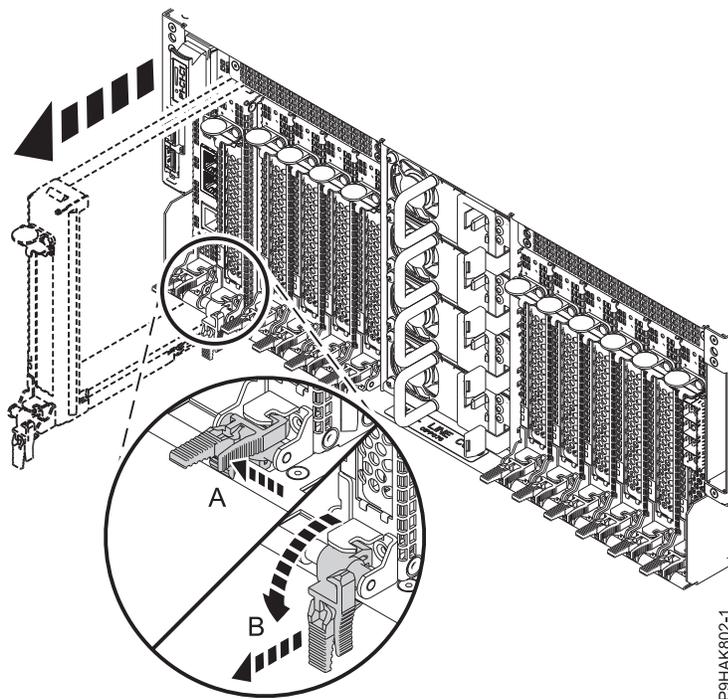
Removendo um cassete do adaptador PCIe do sistema 9040-MR9 ou 9225-50H
